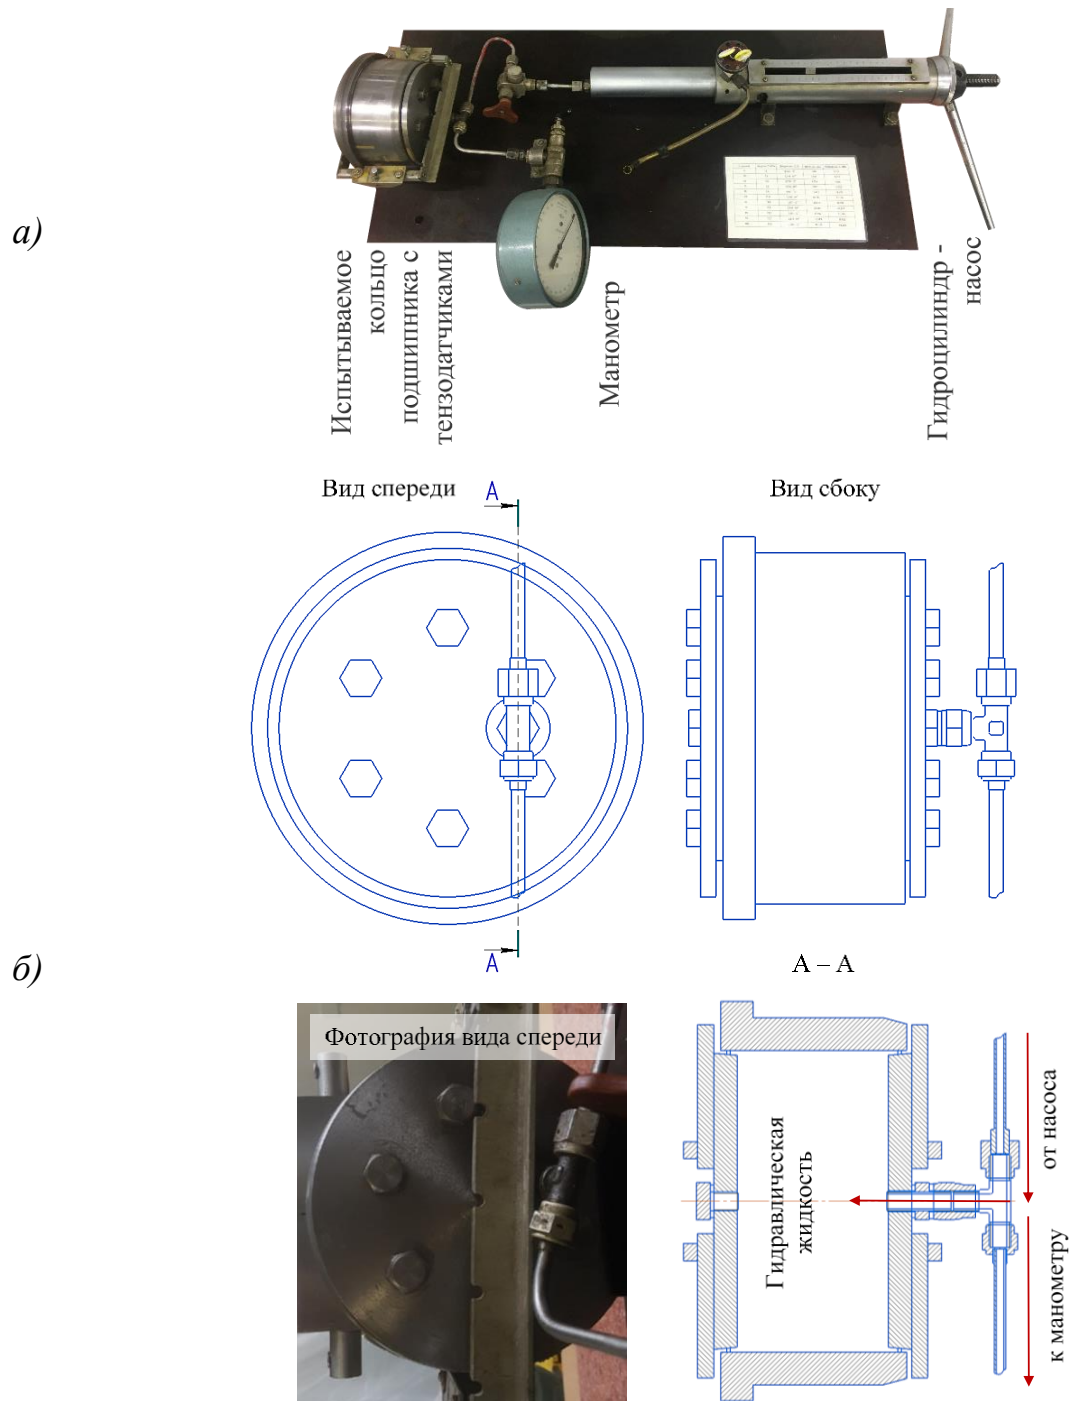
Внешний вид стенда для нагружения колец подшипников (a) и чертеж внутреннего устройства испытательного кольца (б)
